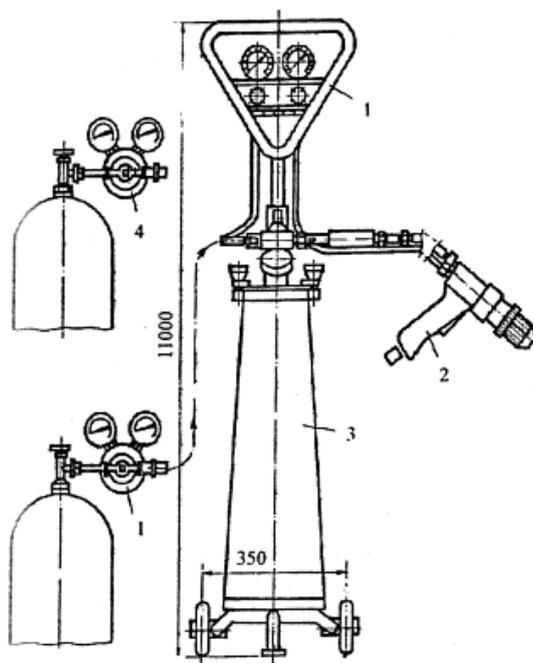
Установка УППЛ: 1 - щит управления; 2 - газопламенный напылитель; 3 - порошковый питатель; 4 - редукторы.
